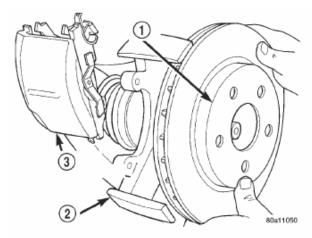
Desmontaje del calibrador del freno de disco y del rotor
